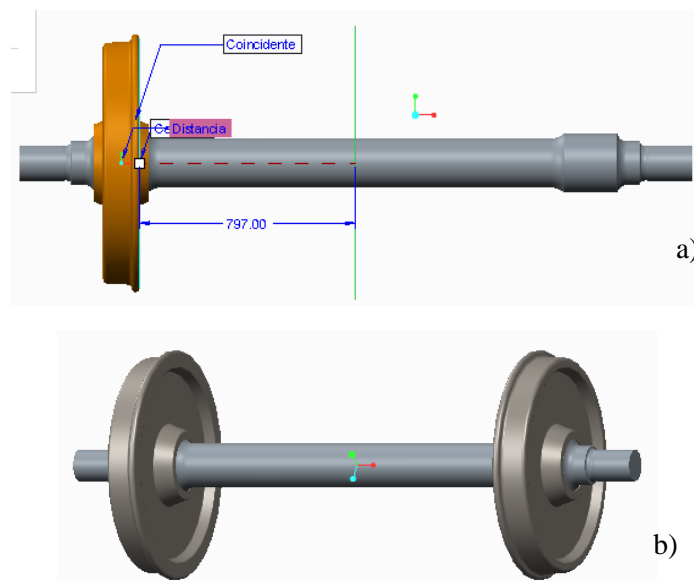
(a) (b) Montaje ruedas sobre eje.
